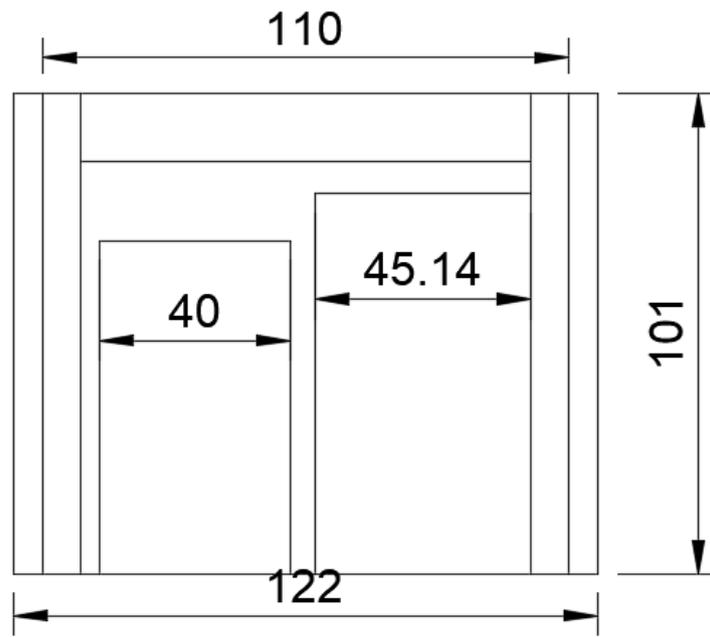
Medidas de la vista superior, parte superior del diseño en 3D
